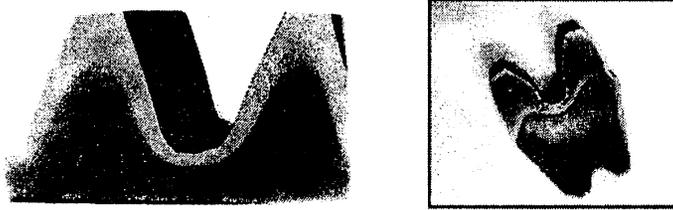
Расположение упрочненной зоны после объемно-поверхностной закалки в сечении зуба ведомой шестерни из стали У8А главной передачи заднего моста – а, и ведущей шестерни колесной передачи из стали 80ПП – б.
